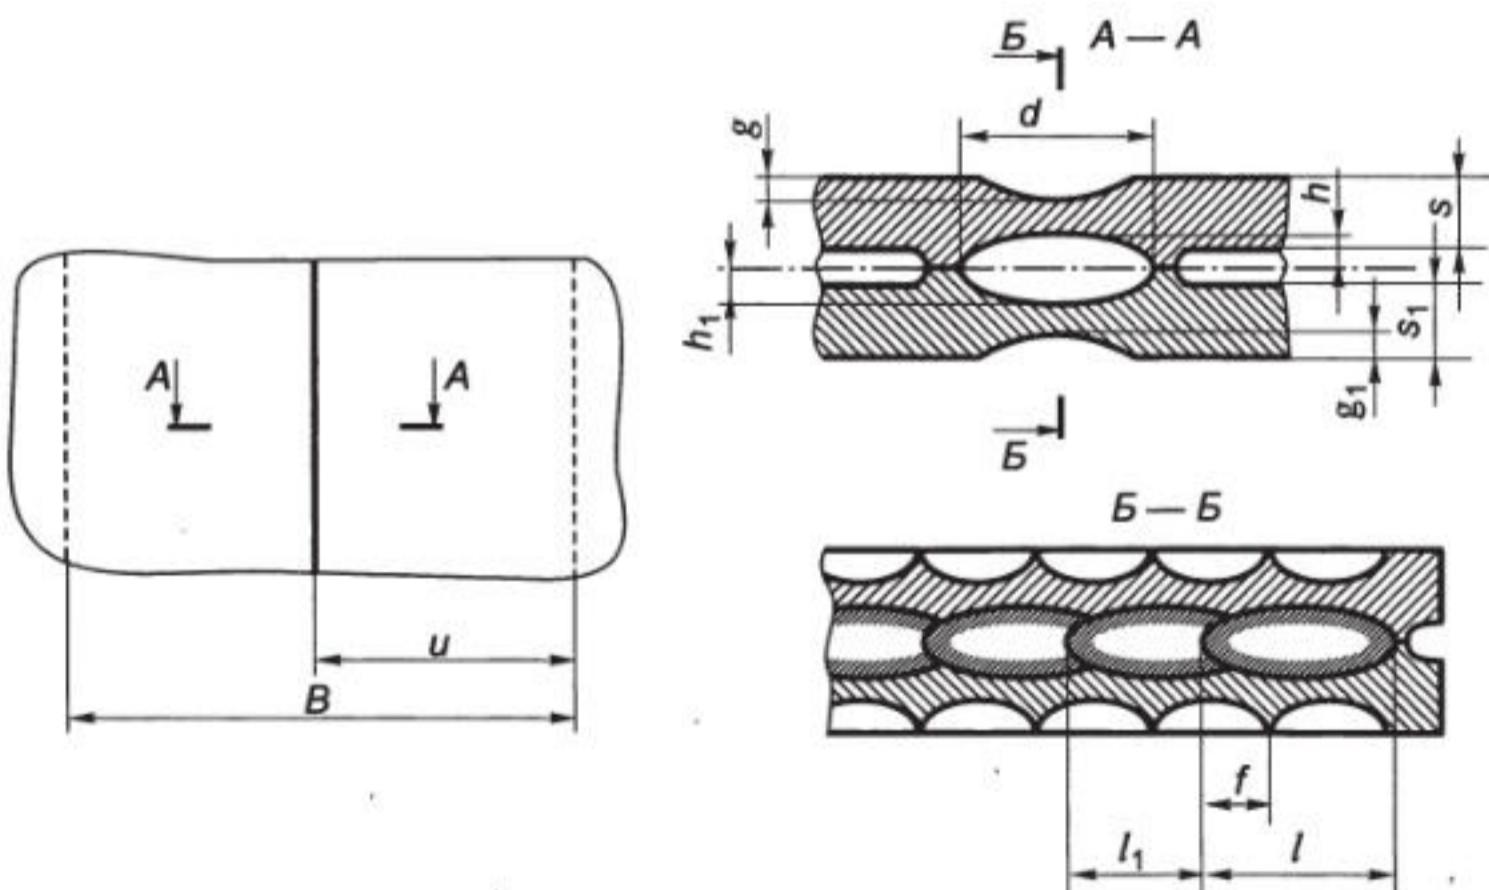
Конструктивные элементы соединений контактной шовной сваркой
